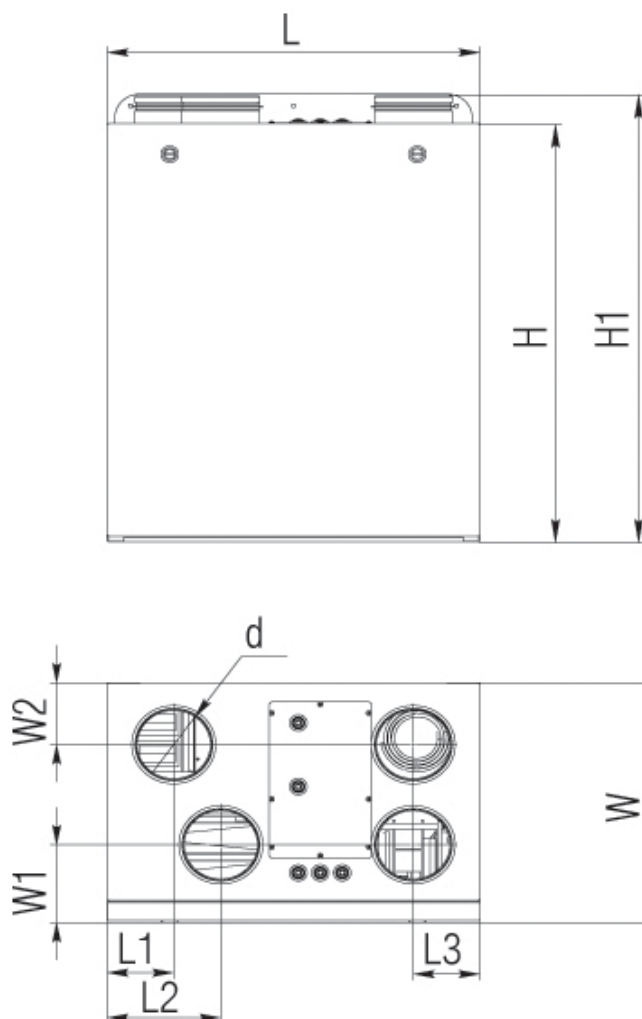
Внешний вид приточно-вытяжной установки SHUFT
